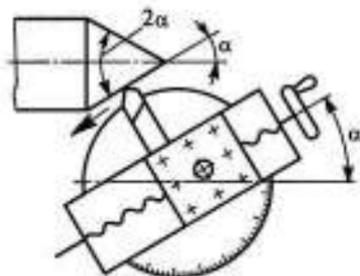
Обработка конической поверхности путем поворота верхних салазок суппорта:
